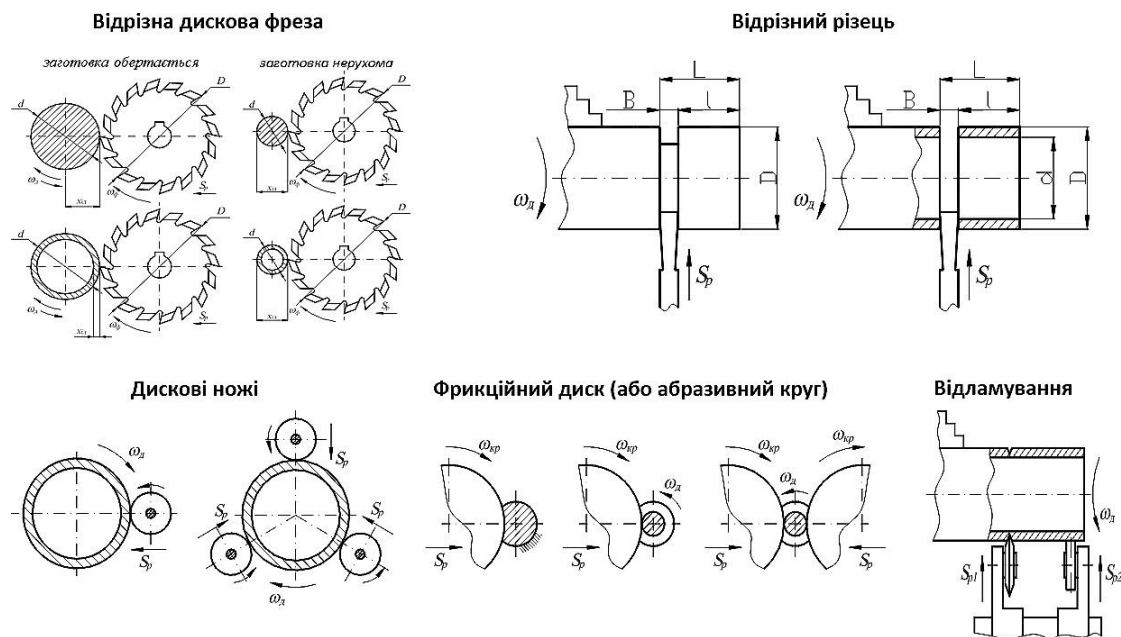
Способи порізки прутково-трубних заготовок класичними методами в металообробці
